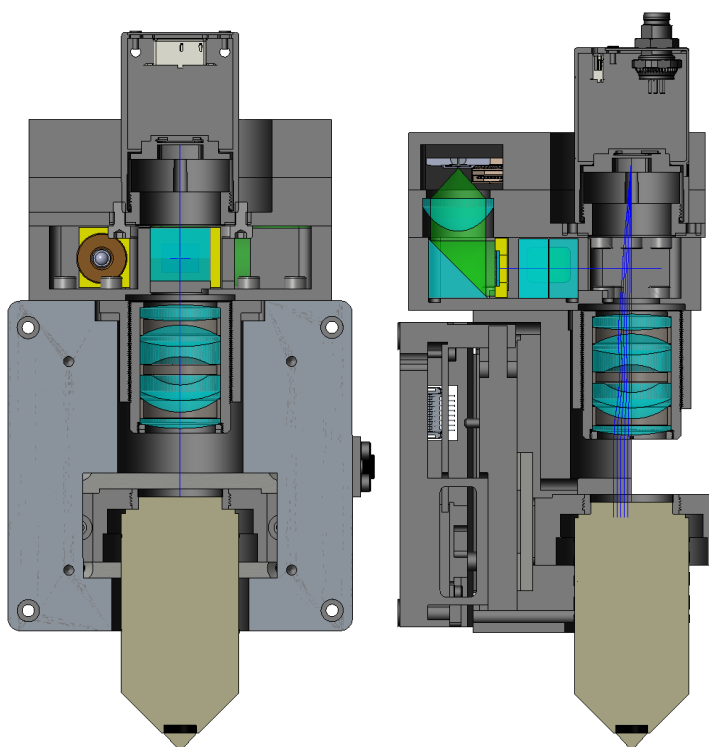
Secció frontal (esquerra) i lateral (dreta) de la Figura 3.18.
